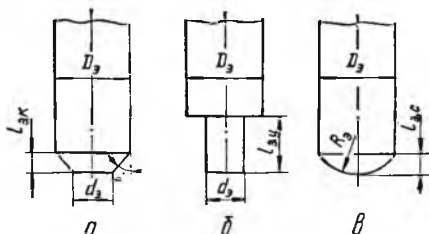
Основные формы рабочих частей электродов для точечной контактной сварки сопротивлением металлических листов:
